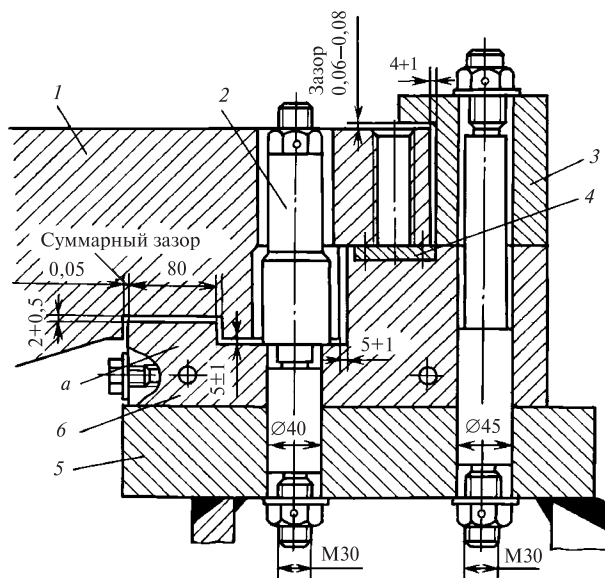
Узел сопряжения лапы и корпуса подшипника в турбине Т-250/300-23,5 ТМЗ:
